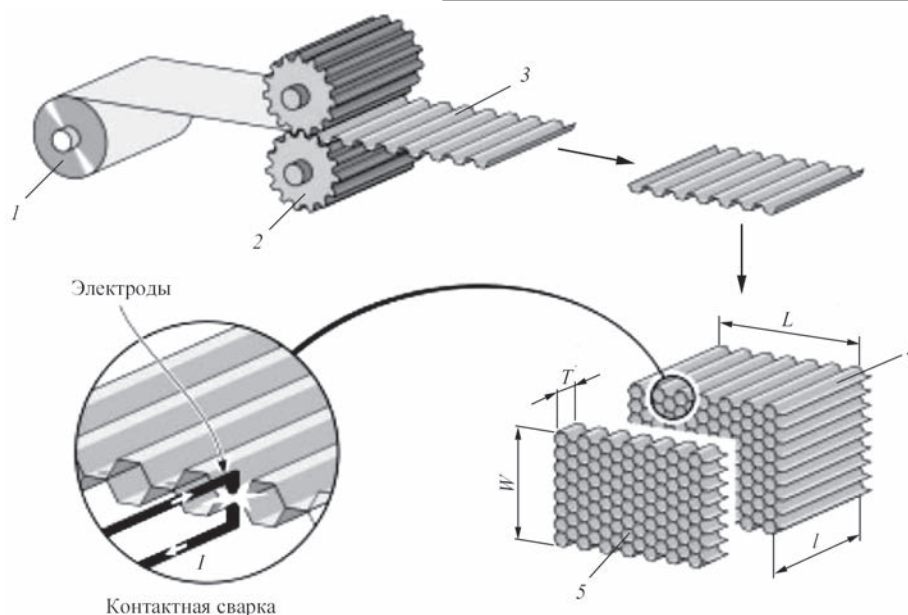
Процесс изготовления сотового заполнителя из профилированных лент [9]: 1 — рулон фольги; 2 — формирующие ролики; 3 — гофрированная фольга; 4 — пакет сотовых заполнителей; 5 — сотовый заполнитель
